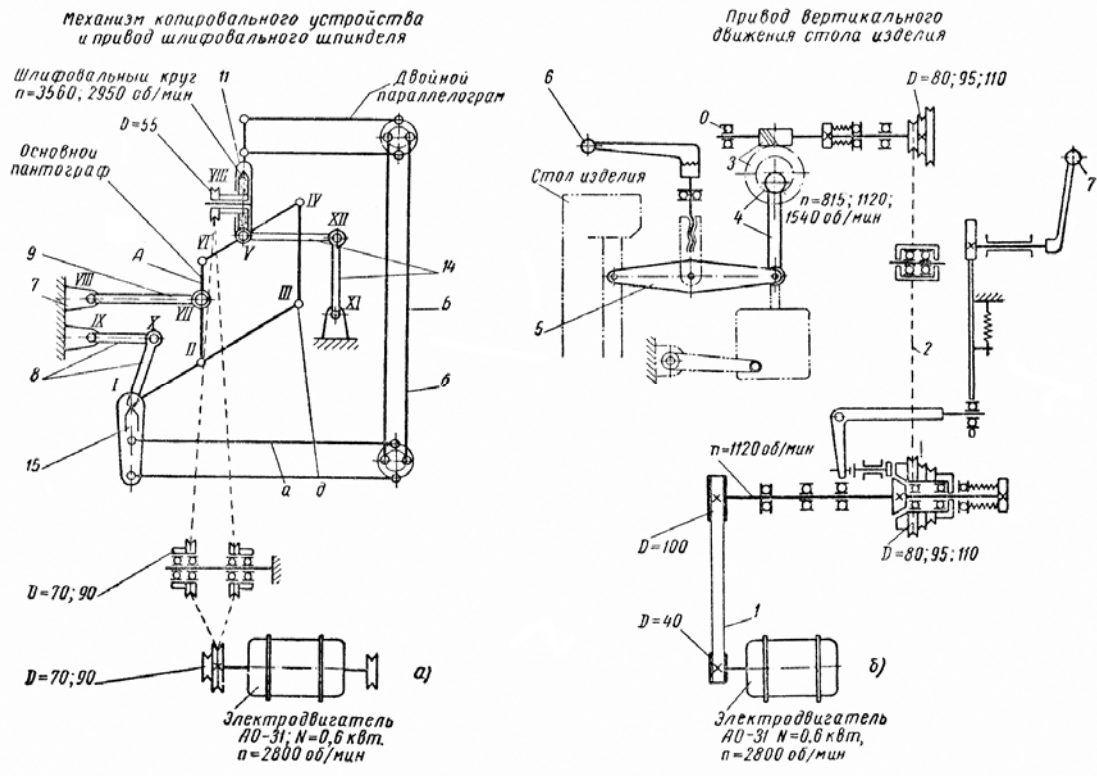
Кинематическая схема профилешлифовального станка мод. Ш-228
